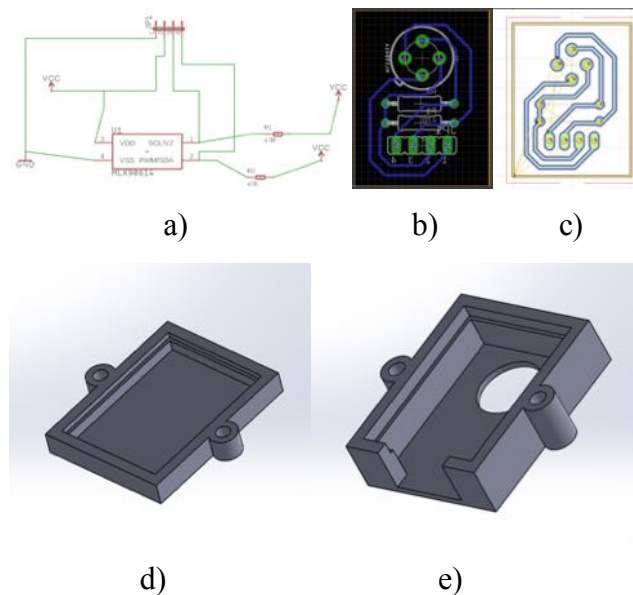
Desenho esquemático, *layout* de *PCB*, preparação de fabrico e encapsulamento do sensor PIR. a) Desenho do esquemático em *Eagle*; b) Organização de vias em *Eagle*; c) Preparação de corte via fresagem *CNC* de *PCB* no *software FlatCam*; d) Desenho da tampa traseira do sensor *PIR*; e) Desenho da tampa frontal do sensor *PIR*.
